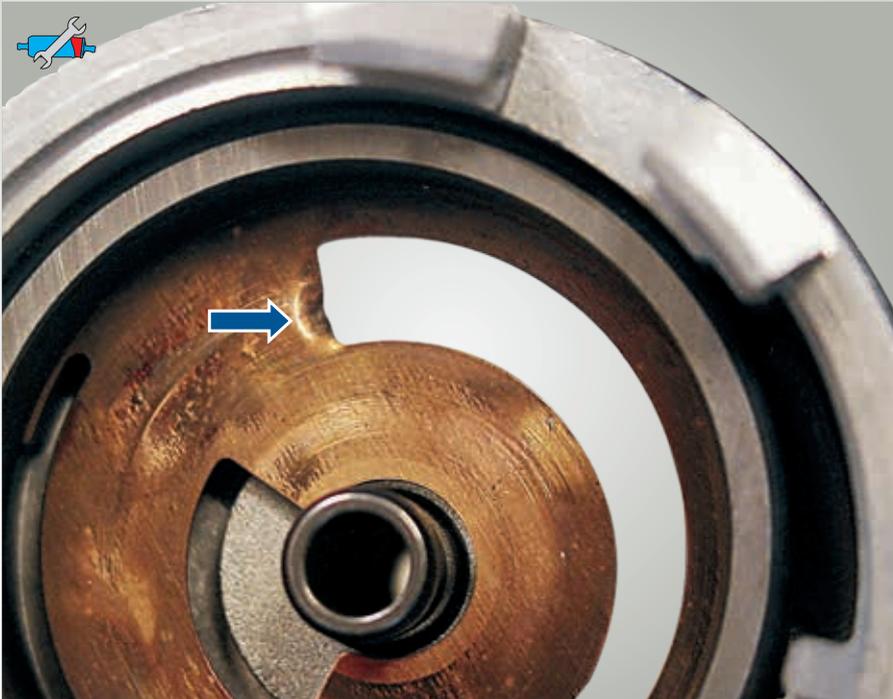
Pompe à engrenage E2T – Dégâts provoqués par des corps étrangers
